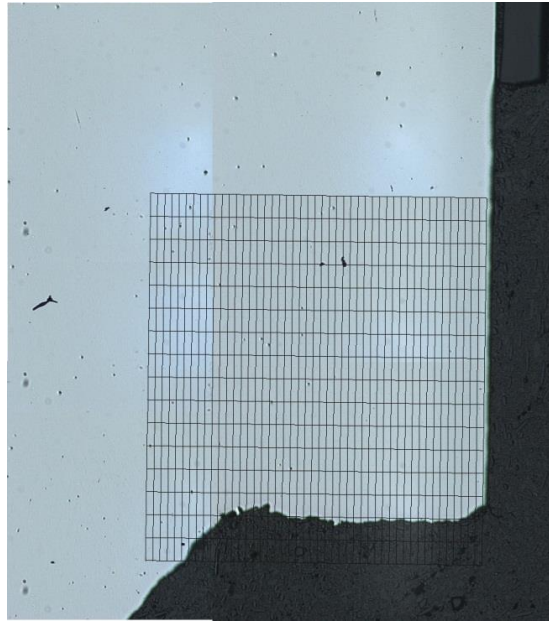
Querschliff von Probe O (siehe Abb. 84); eingezeichnet ist das Messgitter, dessen Gitterpunkte die Eindruckpositionen der Härtemessung angeben.
